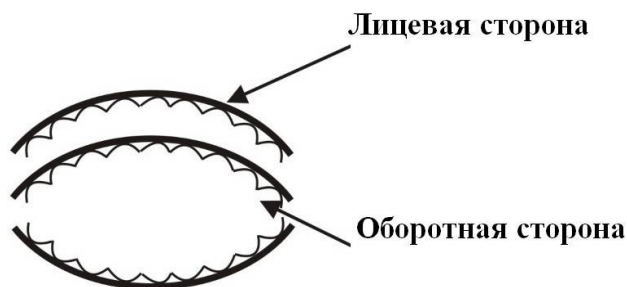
Схема сборки пакета из листов шпона трехслойной фанеры
